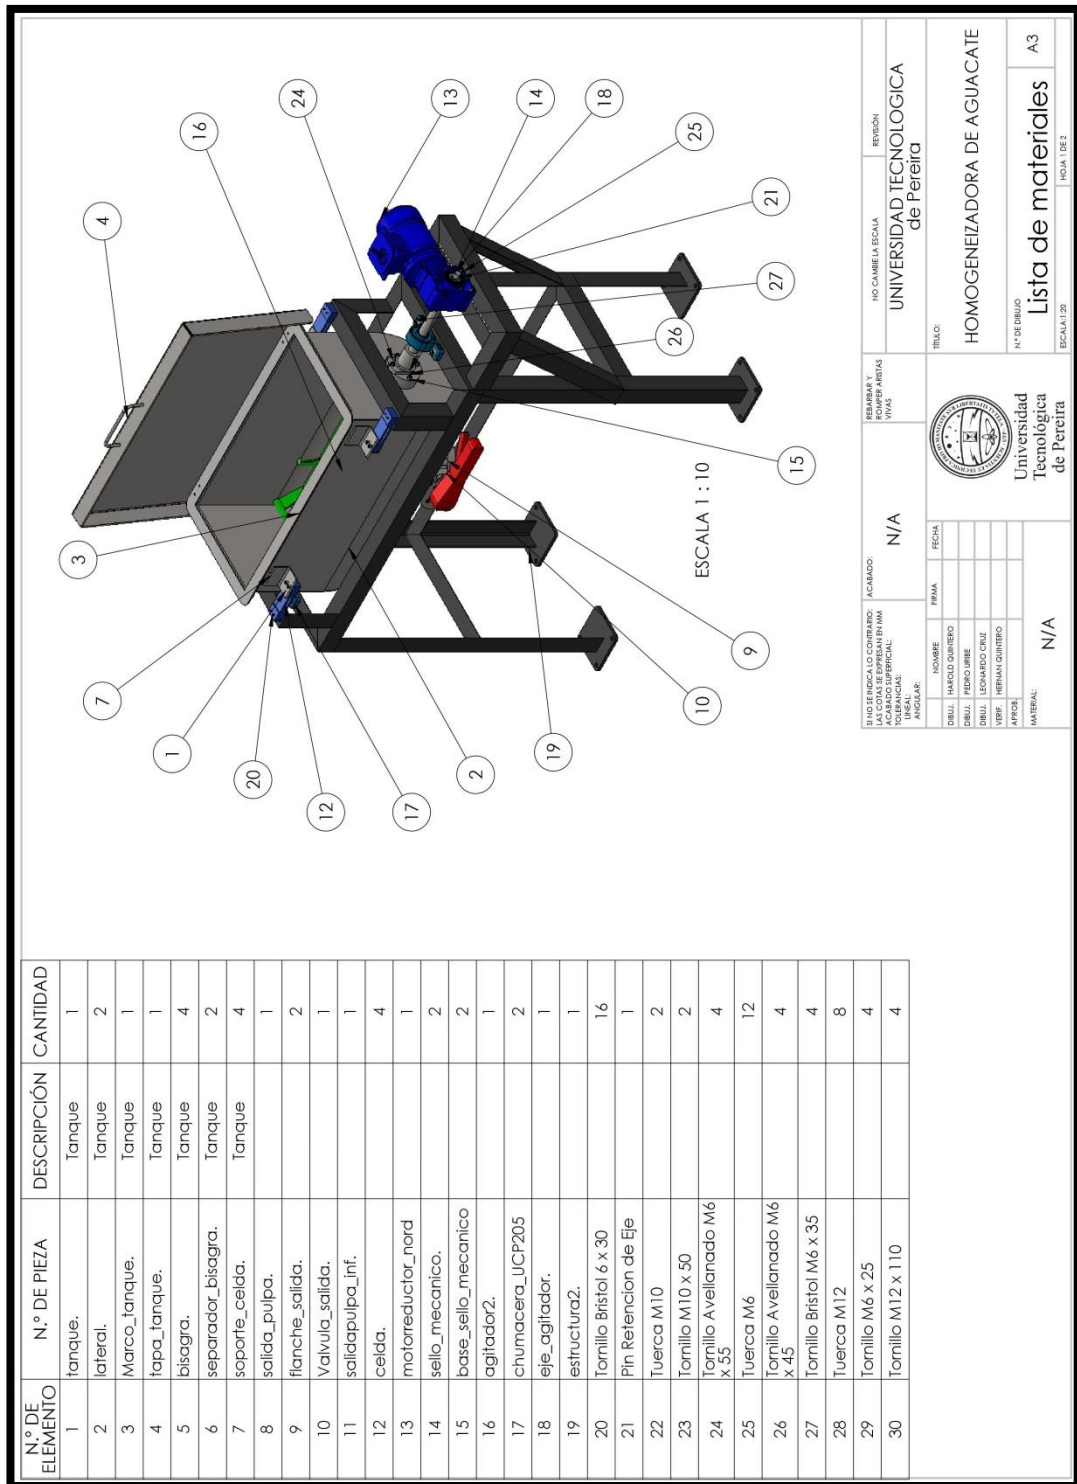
Listado de piezas del equipo.<sup>37</sup>
